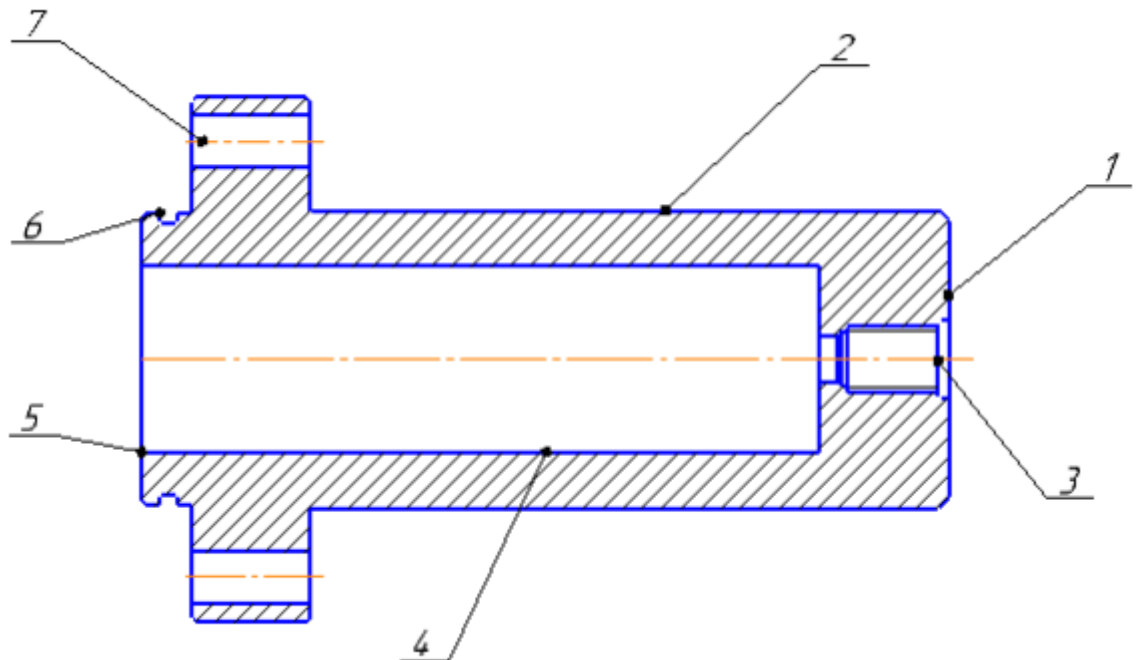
Креслення оброблюваної деталі з необхідними розмірами
